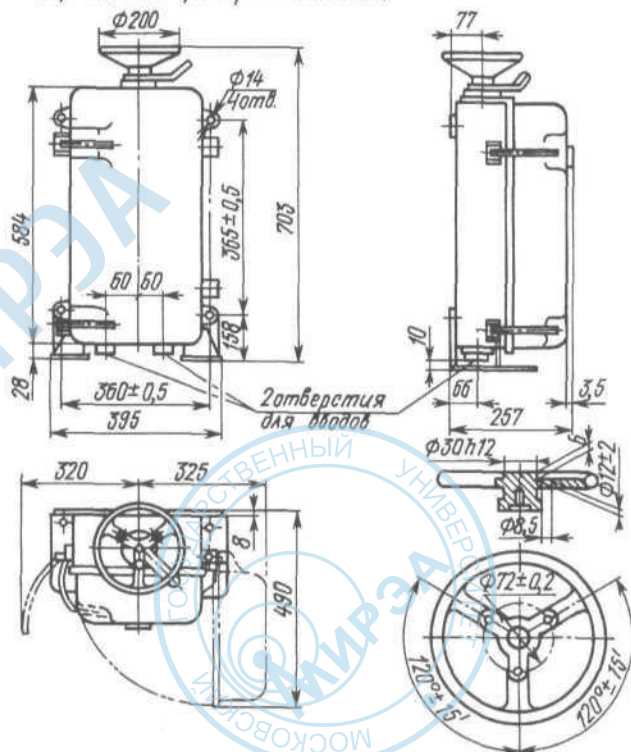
Габаритные, установочные размеры и масса контроллеров КВ-1000А
